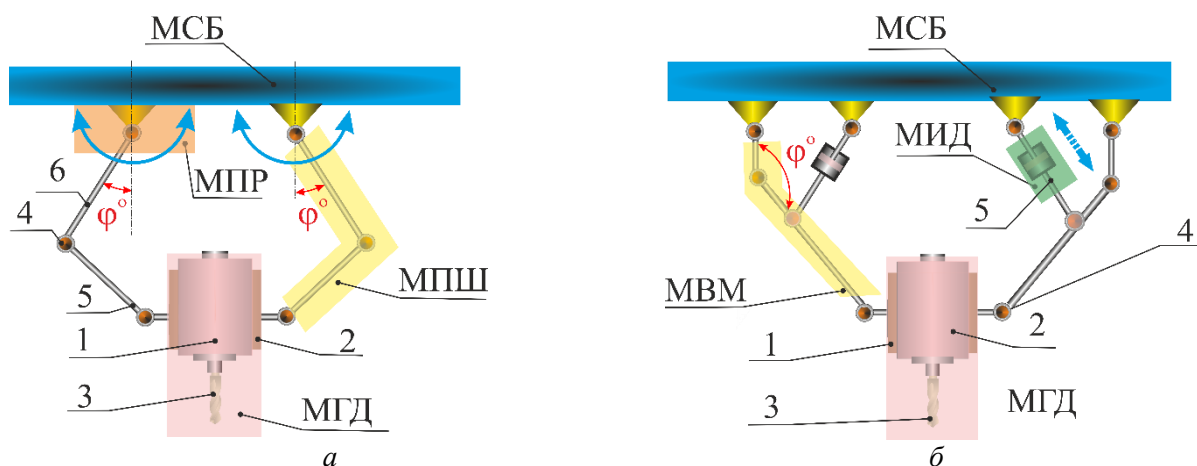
Механизмы с принудительным вращательным движением опорного шарнира (а) и с V-образным МПС (б): 1 – ИО; 2 – привод главного движения; 3 – инструмент; 4 – шарнир; 5,6 – штанги
